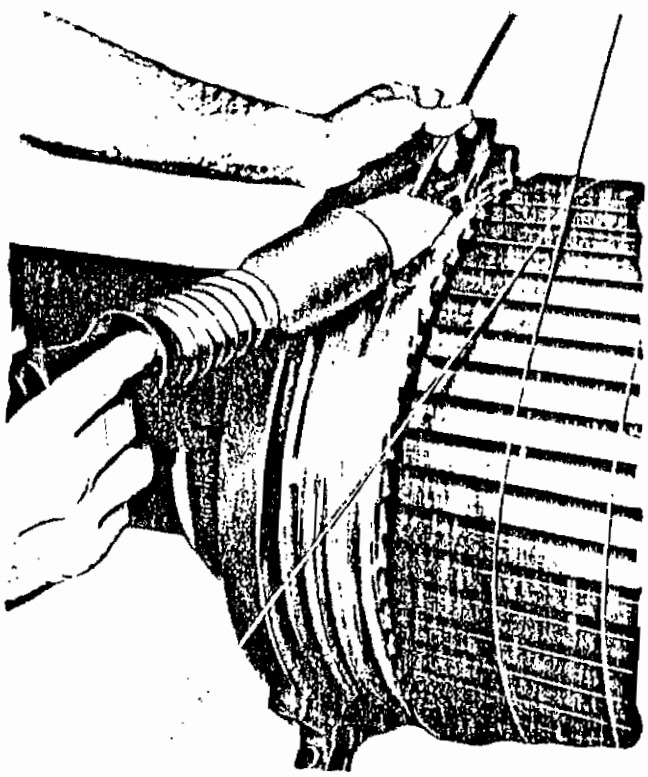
Soldadura de las grapas y del alambre de banda juntos con soldadura de plata
